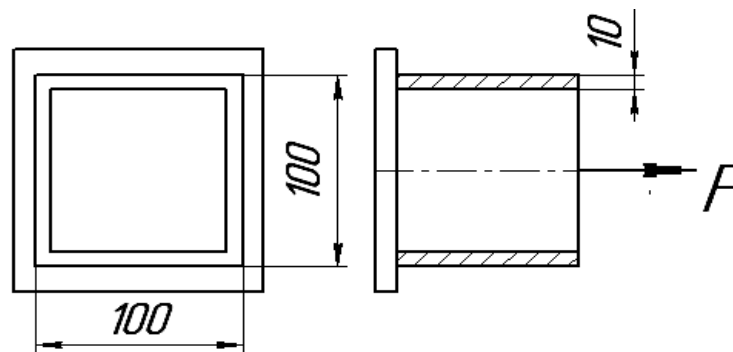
Сварное соединение, выполненное тавровыми сварными швами
